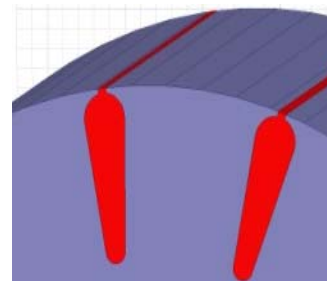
Ротор асинхронного двигателя с кольцевыми обмотками
